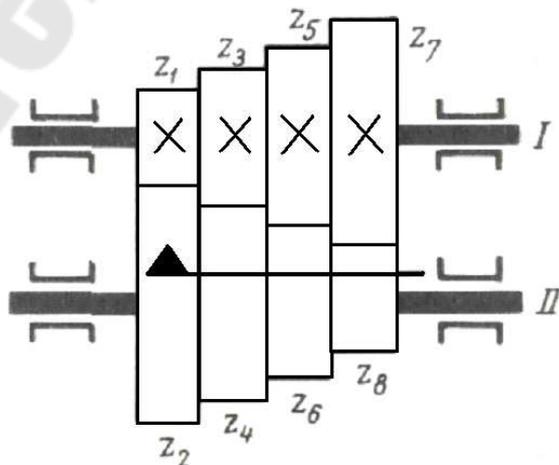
Схема шестерёнчатой коробка передач с выдвигной шпонкой
